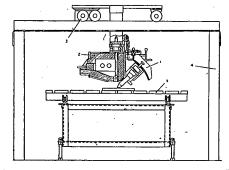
Schweißmaschine von Nikitin (Erläuterung siehe Text)
